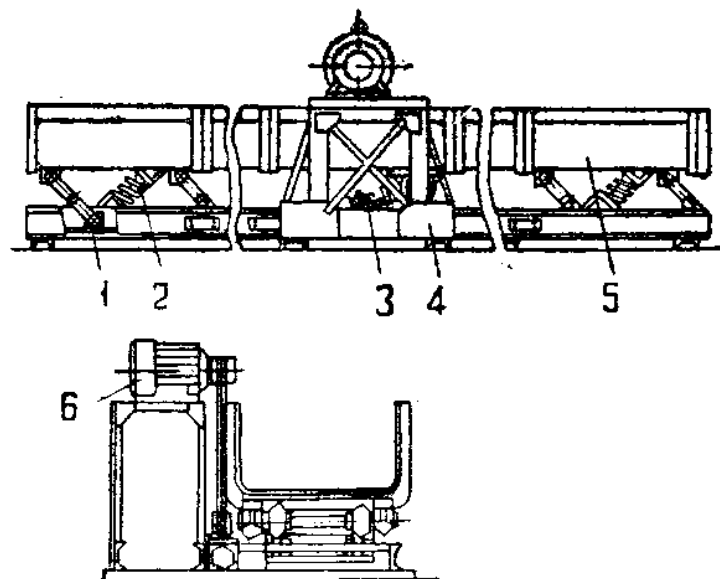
Принципова схема вібраційного конвеєра ВК-1:
